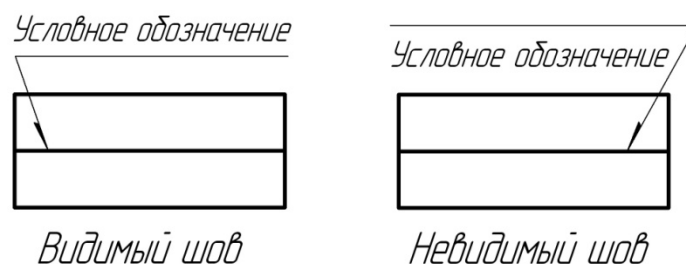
Размещение условного обозначения шва с лицевой и обратной стороны
